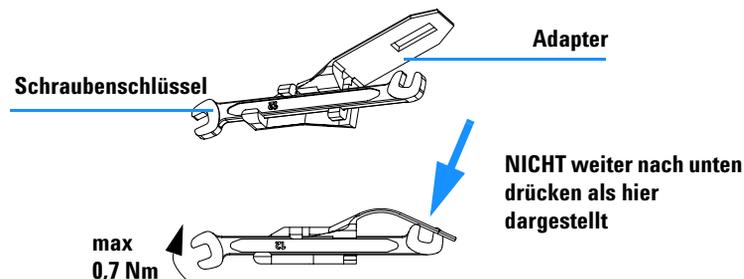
Schraubenschlüssel und Drehmomentadapter
